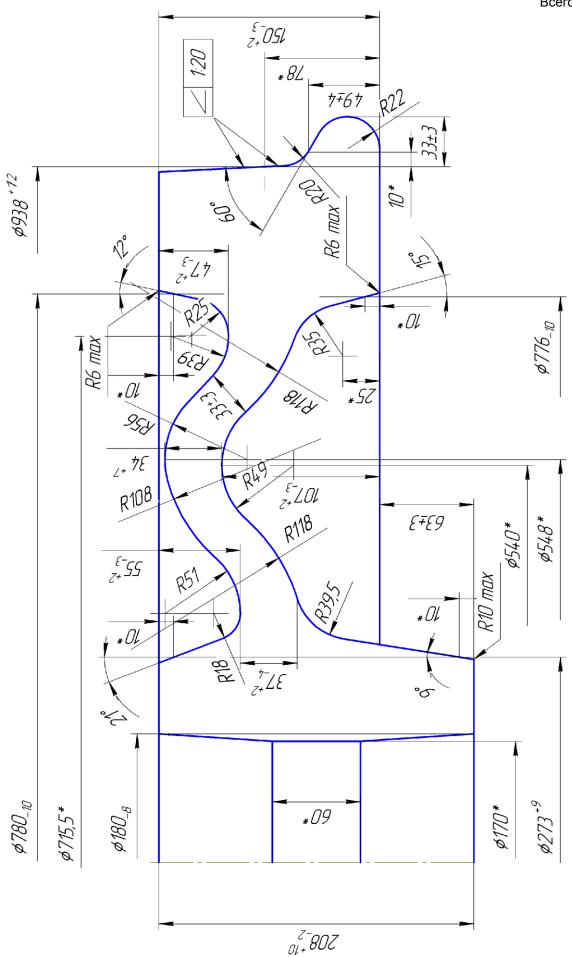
Колесо черновое Ø 942 мм под Ø 920 мм, черт. №КР-0073-15 Масса чернового колеса на 2/3 поля допуска = 531 кг.
